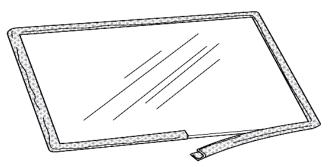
Application du joint d'étanchéité (pièce n° 129124).
